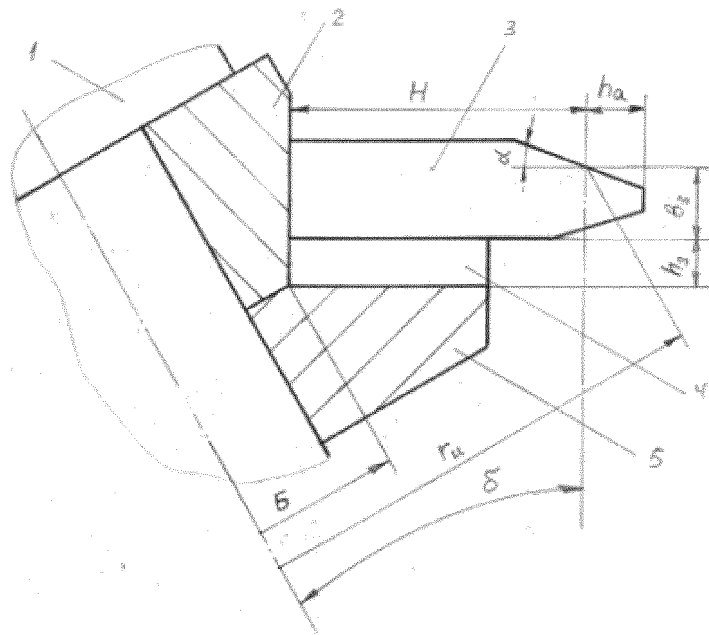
Розташування зовнішнього різця в пазу корпуса головки
